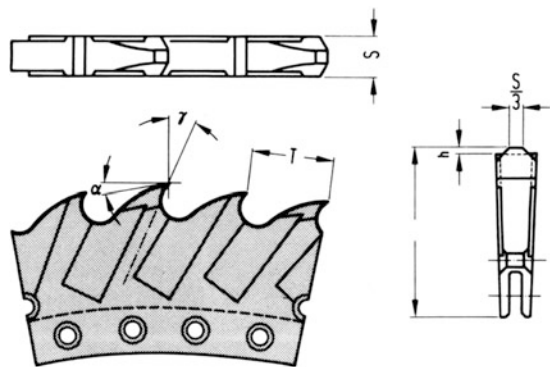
Befestigung des Segmentes im Stammblatt
